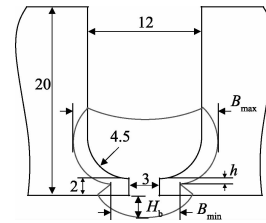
坡口尺寸及焊缝形状参数(单位:mm)
